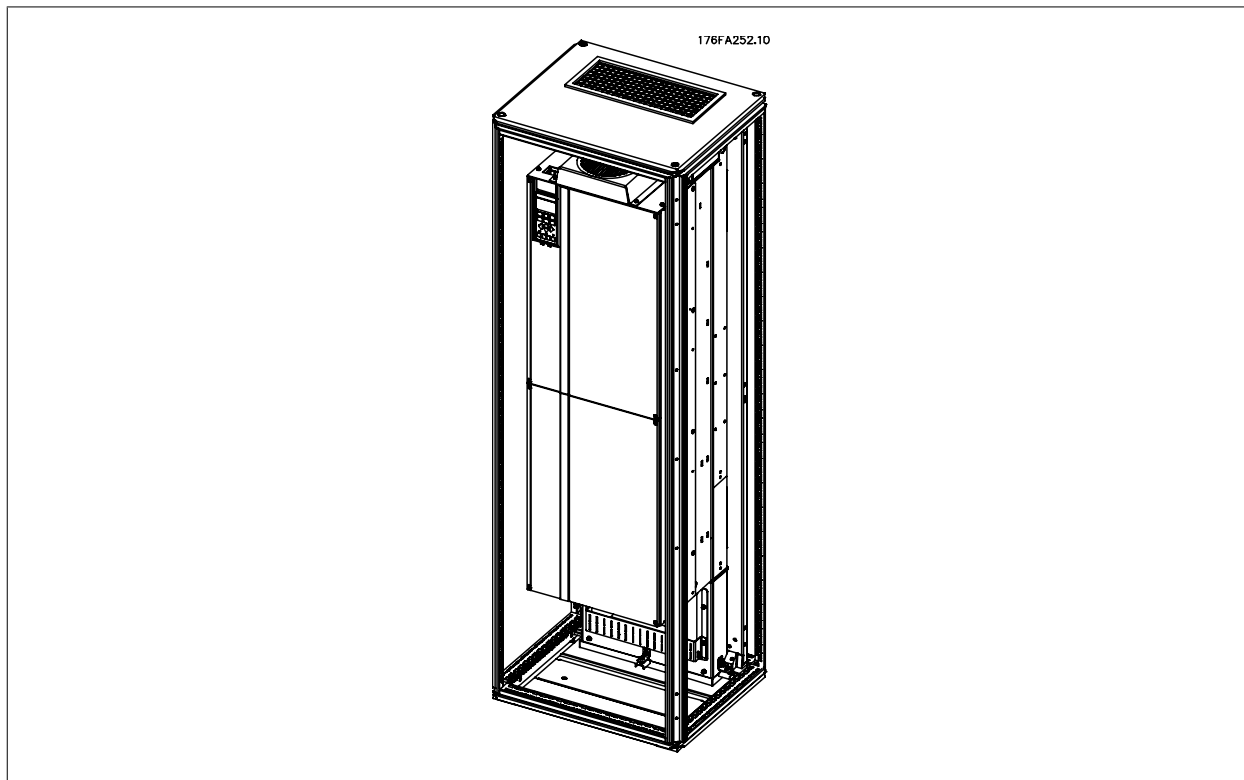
Монтаж блока IP00 в корпусе Rittal TS8
